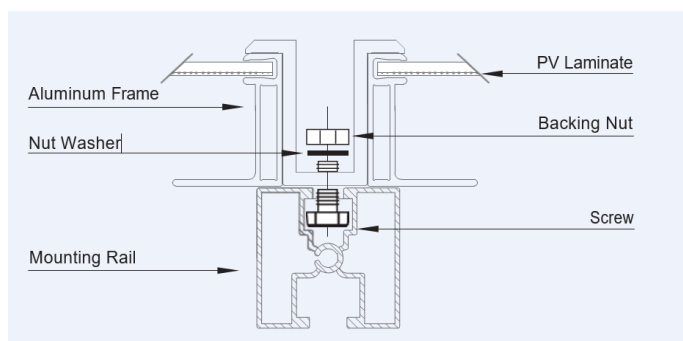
Vue détaillée d'un montage avec étriers de fixation verticaux
